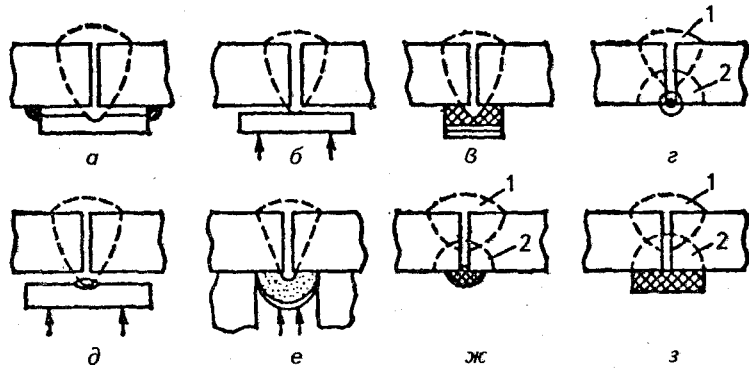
Схемы устройств для удержания сварочной ванны и шлака при сварке под флюсом: а — остающаяся подкладка; б — временная подкладка; в — гибкая лента; г — ручная подварка; д — медно-флюсовая подкладка; е — флюсовая подушка; ж — заделка зазора огнестойким материалом; з — асбестовая подкладка; а, б, в, д, е — односторонний шов; г, ж, з — двусторонний шов; 1 — первый шов; 2 — второй шов
